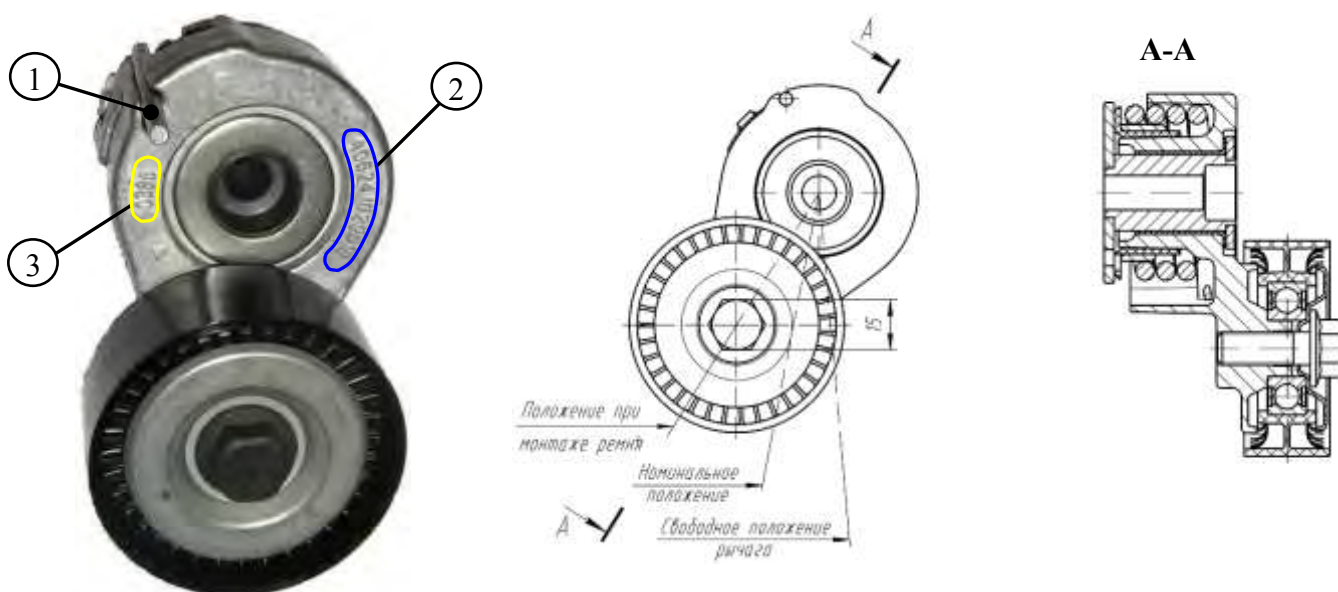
Внешний вид механизма автоматического натяжения ремня:
